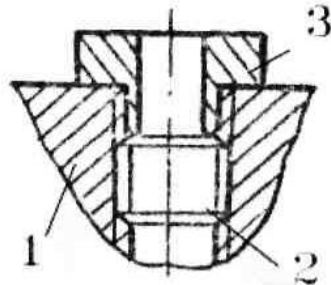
Приварена кондукторна вставка: 1- корпус; 2- залишок обірваної шпильки; 3- кондукторна вставка.
